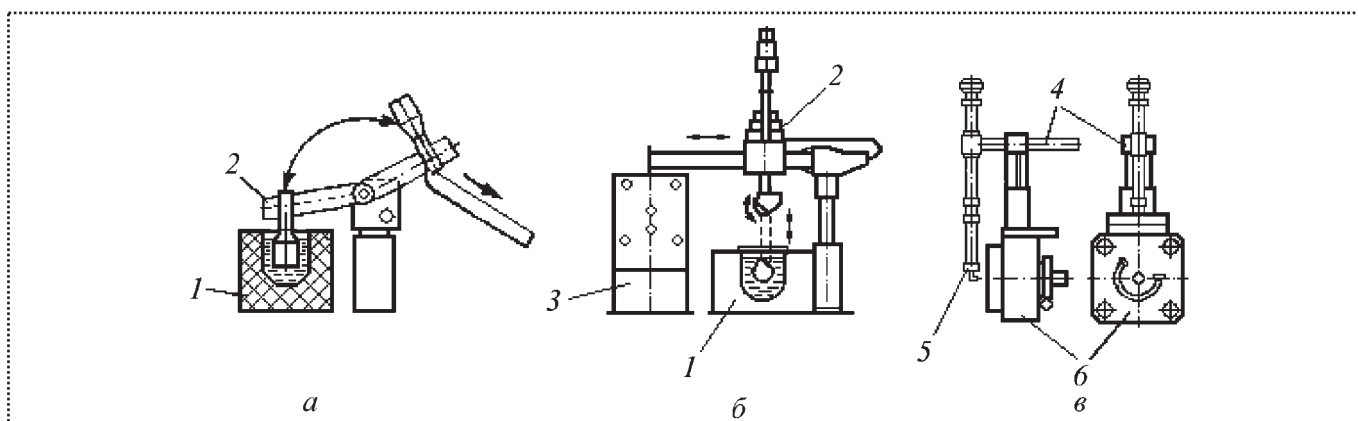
Дозатор-опрокидыватель (а), дозатор портального типа (б) и манипулятор для смазки литейной формы (в): 1 – печь с расплавом; 2 – манипулятор-дозатор; 3 – МЛД; 4 – смазочный манипулятор; 5 – форсунка; 6 – литейная форма
